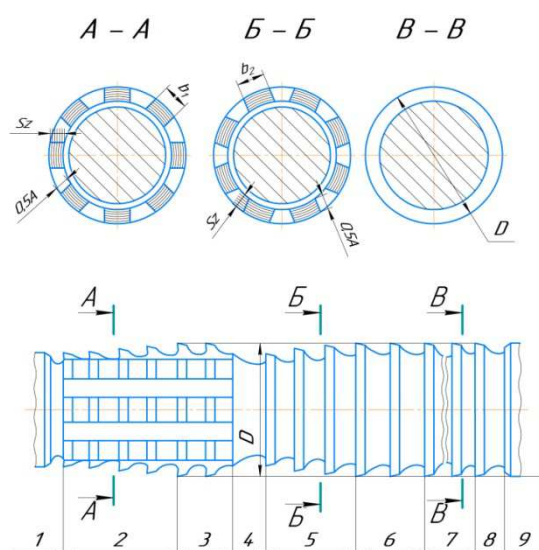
Двухступенчатая прогрессивная протяжка для обработки цилиндрических отверстий
